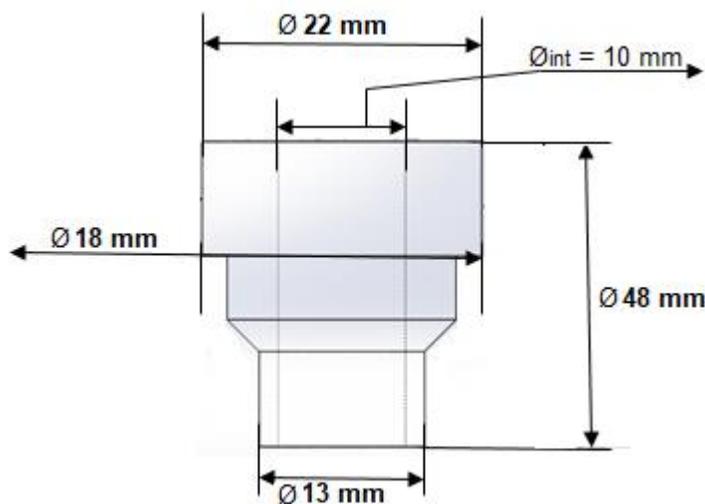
Dimensiones obtenidas de un cilindro usado de bomba lineal
